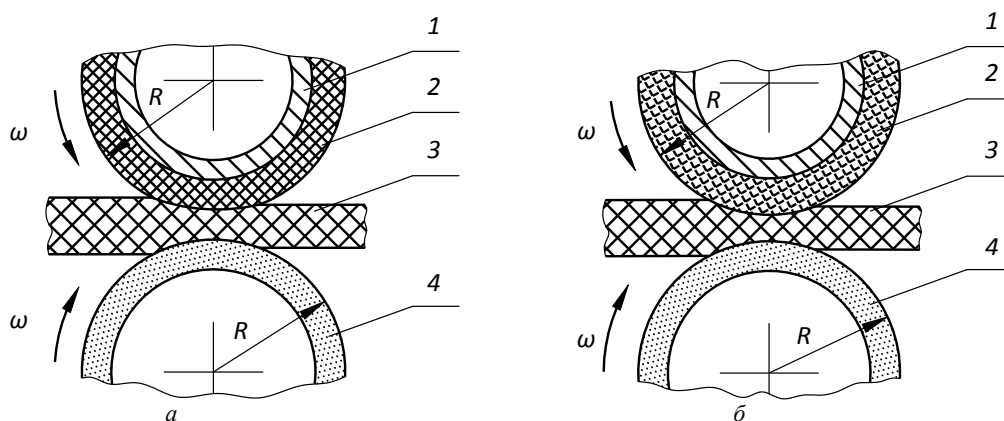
Схема сочетания пар отжимных валов: *а* – 1 – верхний отжимной вал, 2 – покрытие – резина, 3 – кожаный полуфабрикат, 4 – нижний отжимной вал, рабочая часть из пористой металлокерамики; *б* – 1 – верхний отжимной вал, рабочая часть из пористой металлокерамики, 2 – покрытие сукно, 3 – кожаный полуфабрикат, 4 – нижний отжимной вал, рабочая часть из пористой металлокерамики
